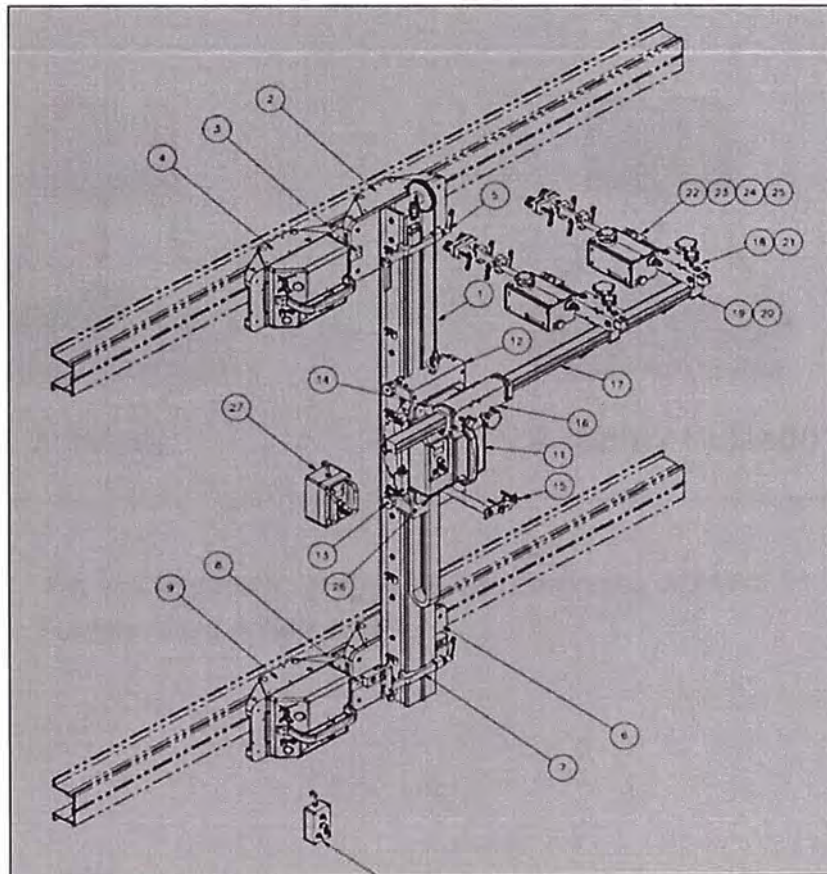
Esquema de soldadura mecanizada GMAW.
